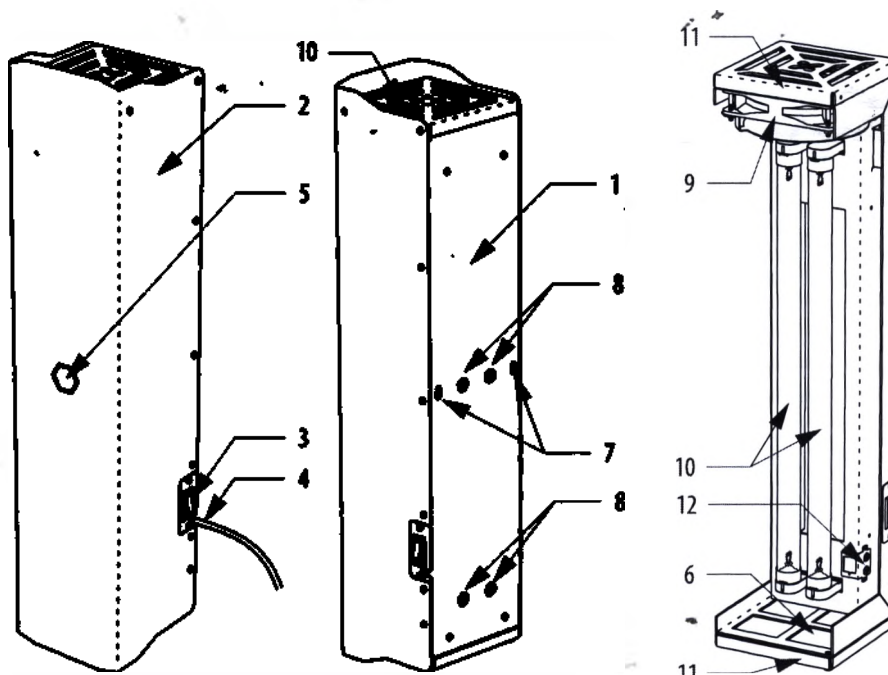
Общая конструкция облучателя-рециркулятора ОВУ-03.
